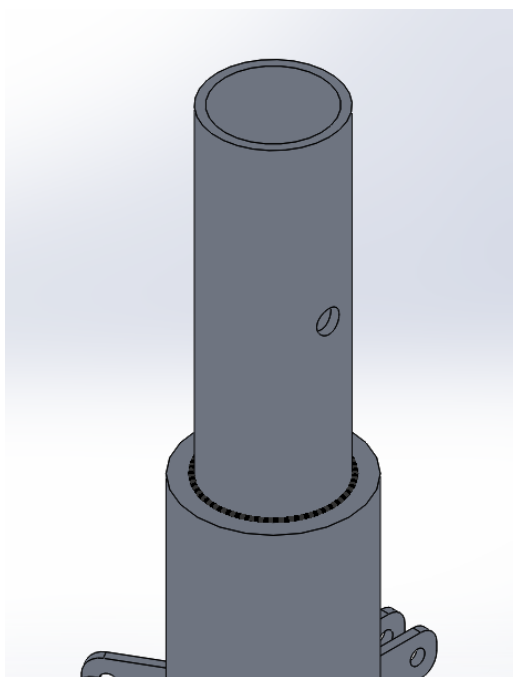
Vista seccionada tub base amb suport per al següent tram format per una “creueta soldada”
